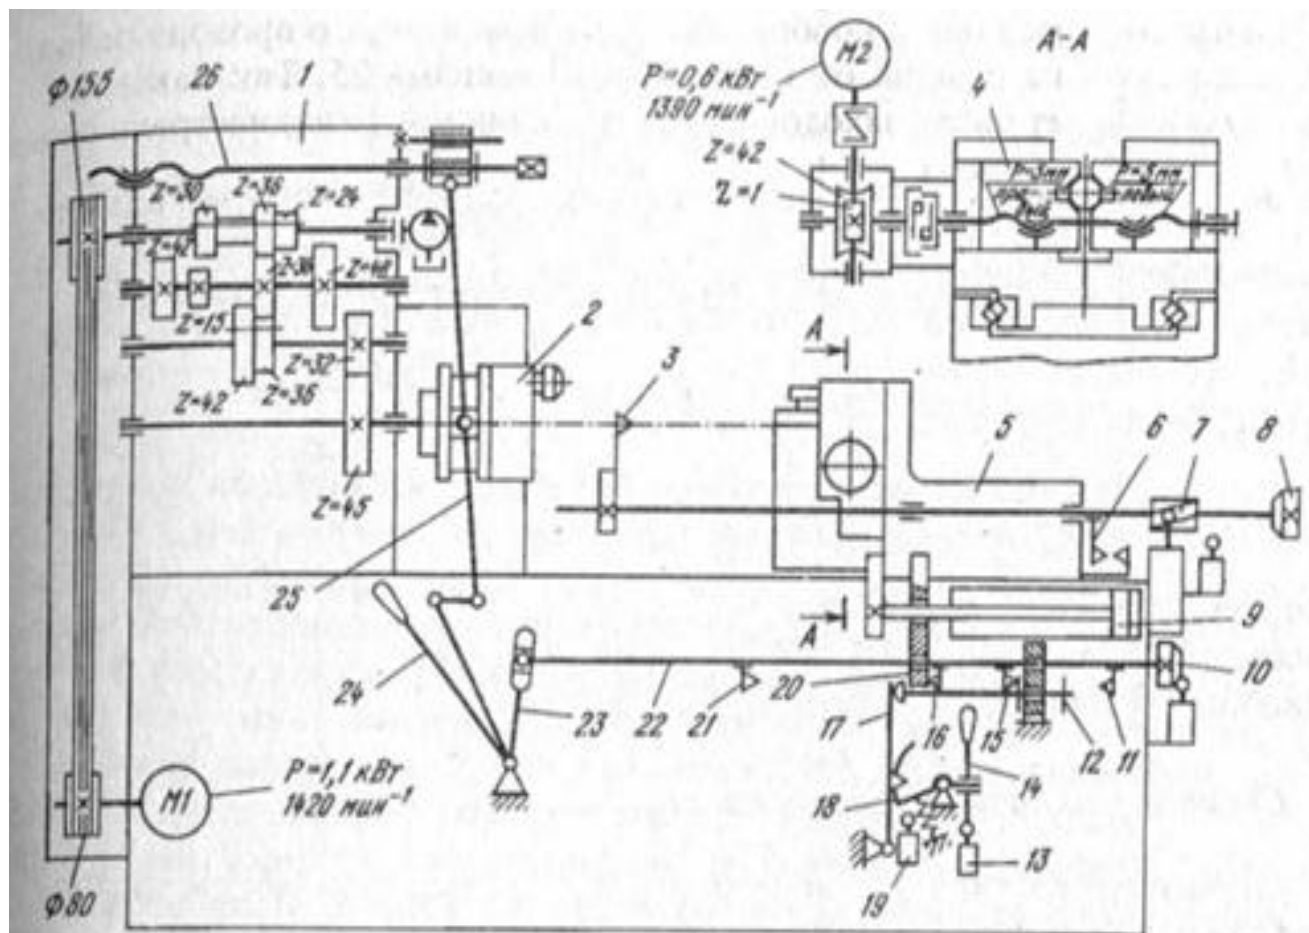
Кинематическая схема резьбонарезного полуавтомата модели 5991.
